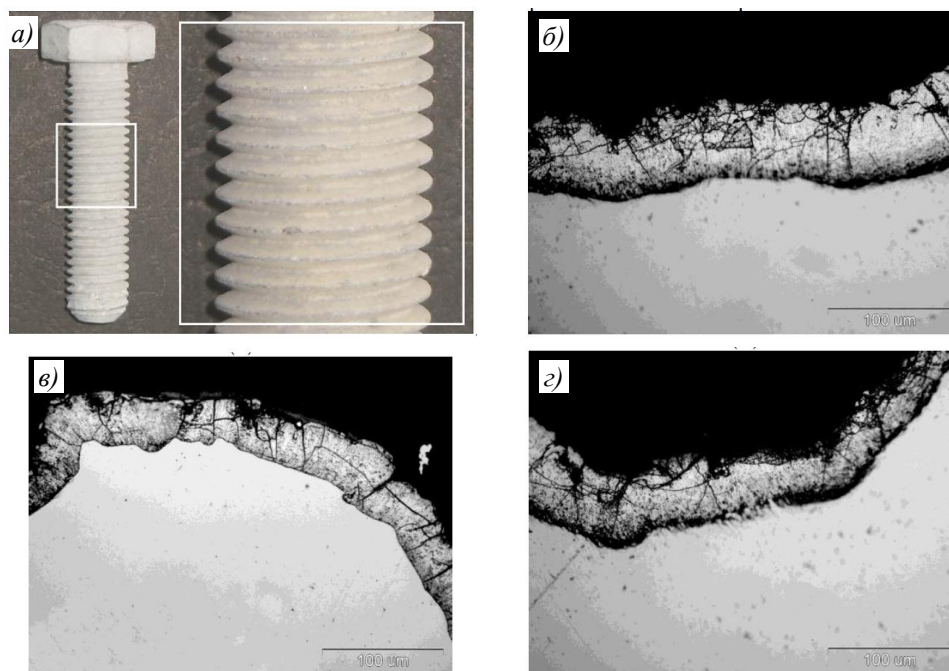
Внешний вид покрытия (а) и поперечные сечения головки болта (б), конца резьбы (в), углубления (з) [42]
